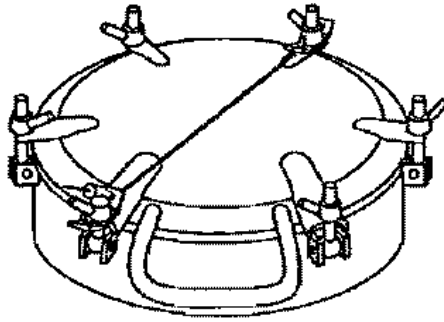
Схема установки универсального ЗПУ с длиной каната 800 и 850 мм на верхней крышке загрузочного люка цистерны барашкового типа, оборудованной "ограничителем хода"
